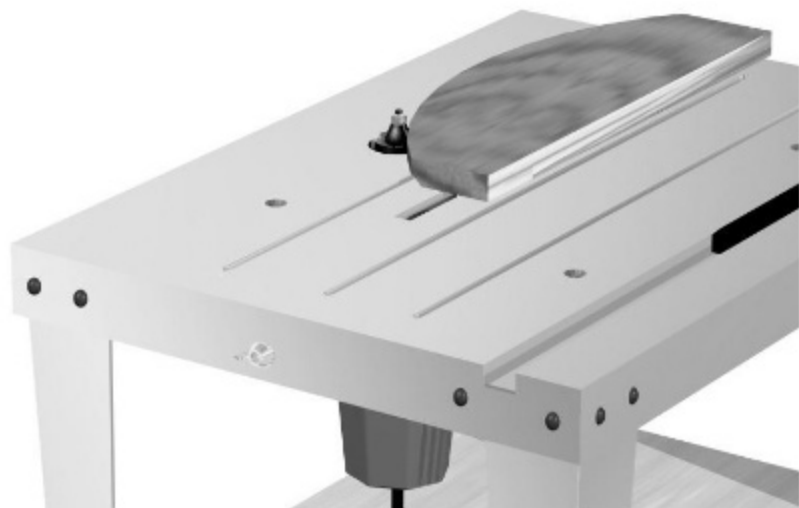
Perfilado de la moldura del respaldo mediante la fresadora, empleada como tulpí
